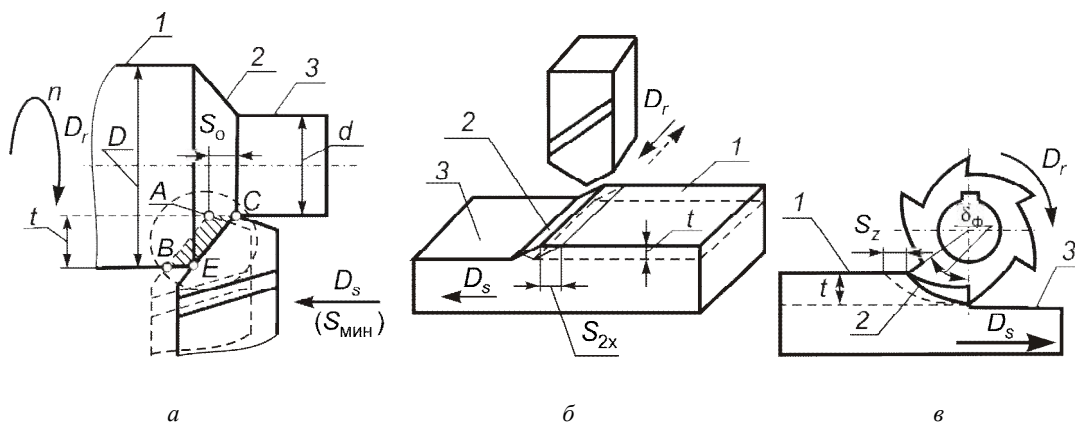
Виды подач при резании лезвийным инструментом: а – подача на оборот при точении S_0 (S); б – подача на двойной ход при строгании S_{2x} ; в – подача на зуб при фрезеровании S_z ; 1 – обрабатываемая поверхность; 2 – поверхность резания; 3 – обработанная поверхность
